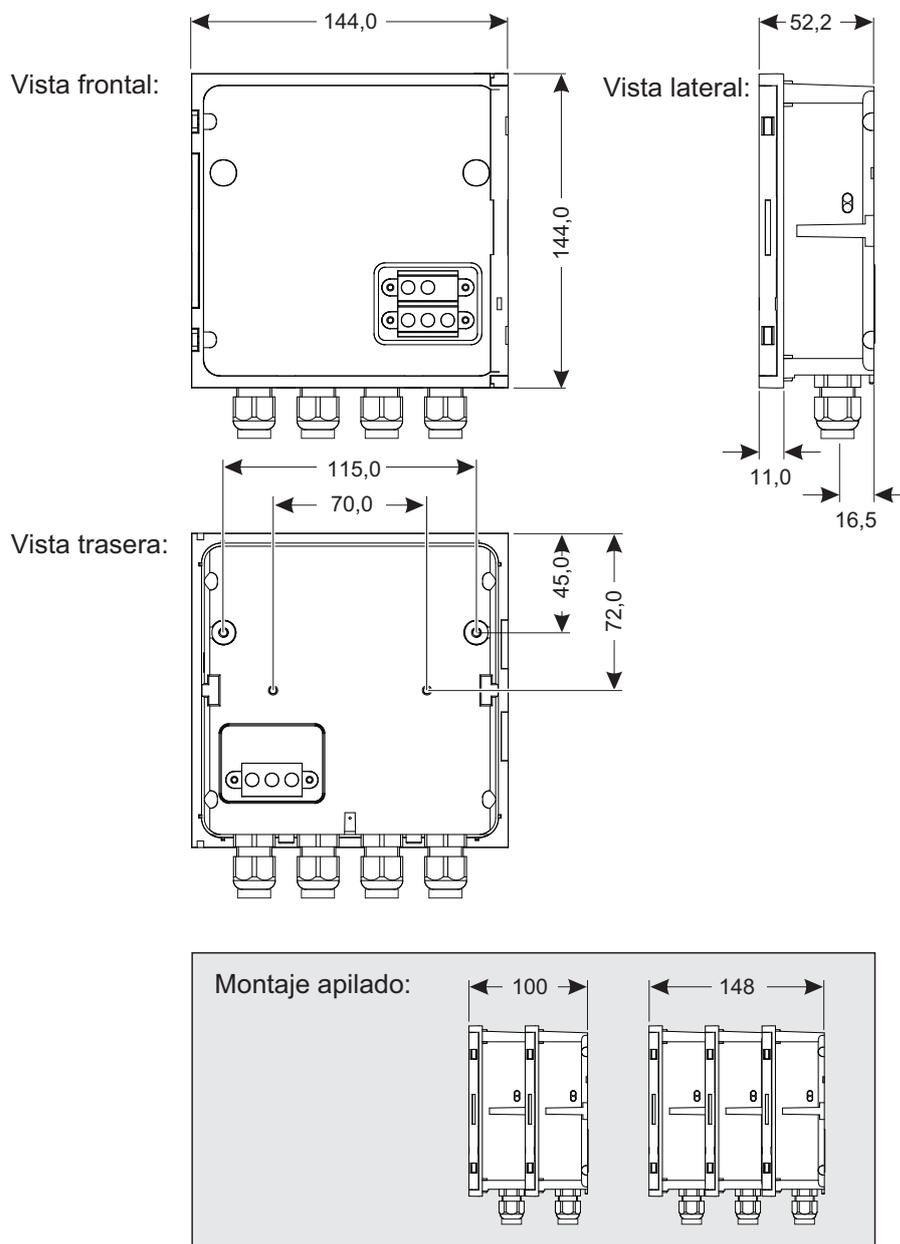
Dibujo acotado del módulo MIQ (dimensiones en mm)
